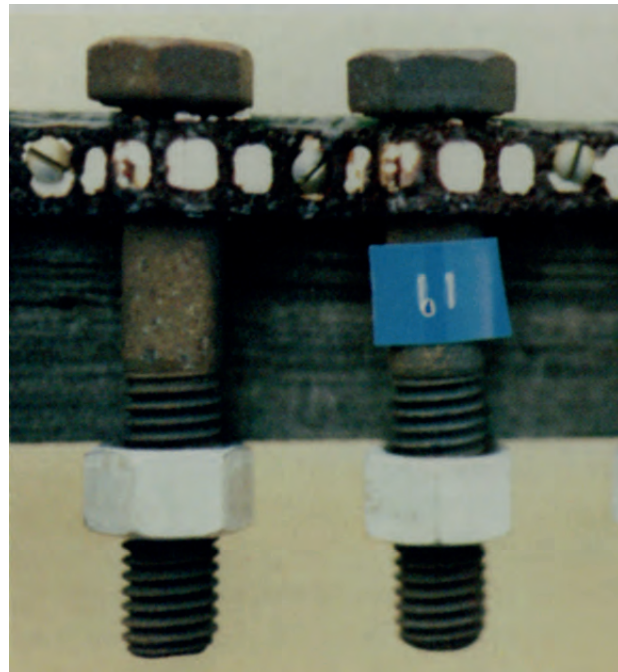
Varmförzinkad skruv med syrafasta muttrar efter 15 års exponering i marin miljö. Obetydlig galvanisk korrosion.
